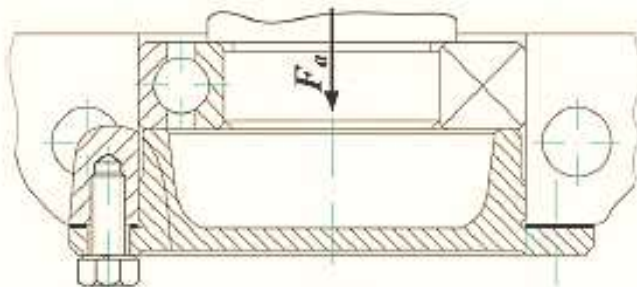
Эскиз к расчету винтового соединения крышки с корпусом редуктора
